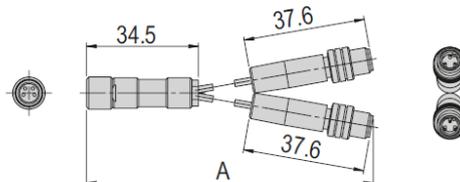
Initiateur – INI c10x19.5-Em-PNP-NO-M8x1 et câble de l'initiateur R10
